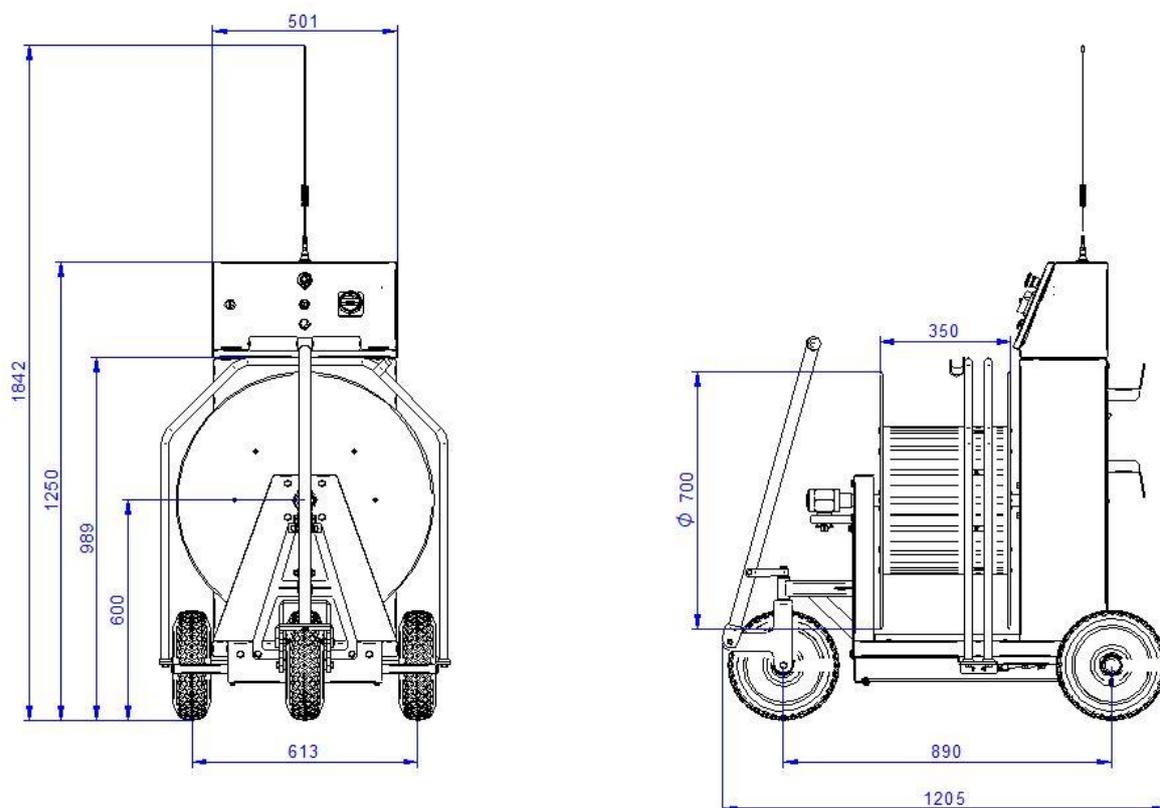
; Dimensioni dell'avvolgitore su pneumatici in mm
